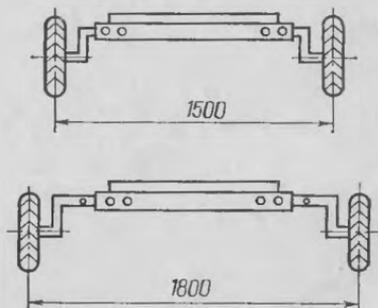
Установка колеи опрыскивателя ОПШ-15-01.
